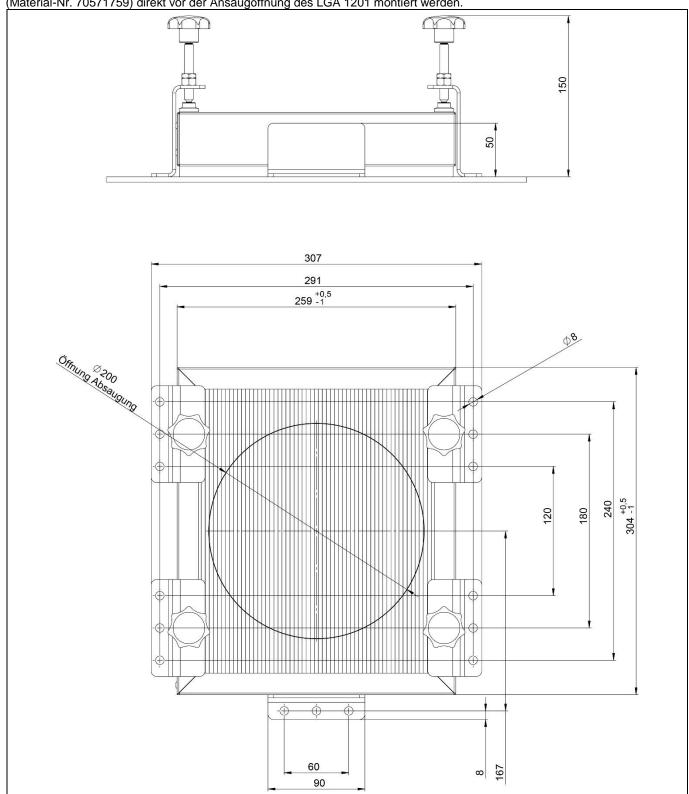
Einbau einer MIO Filterplatte in eine Bearbeitungsmaschine
